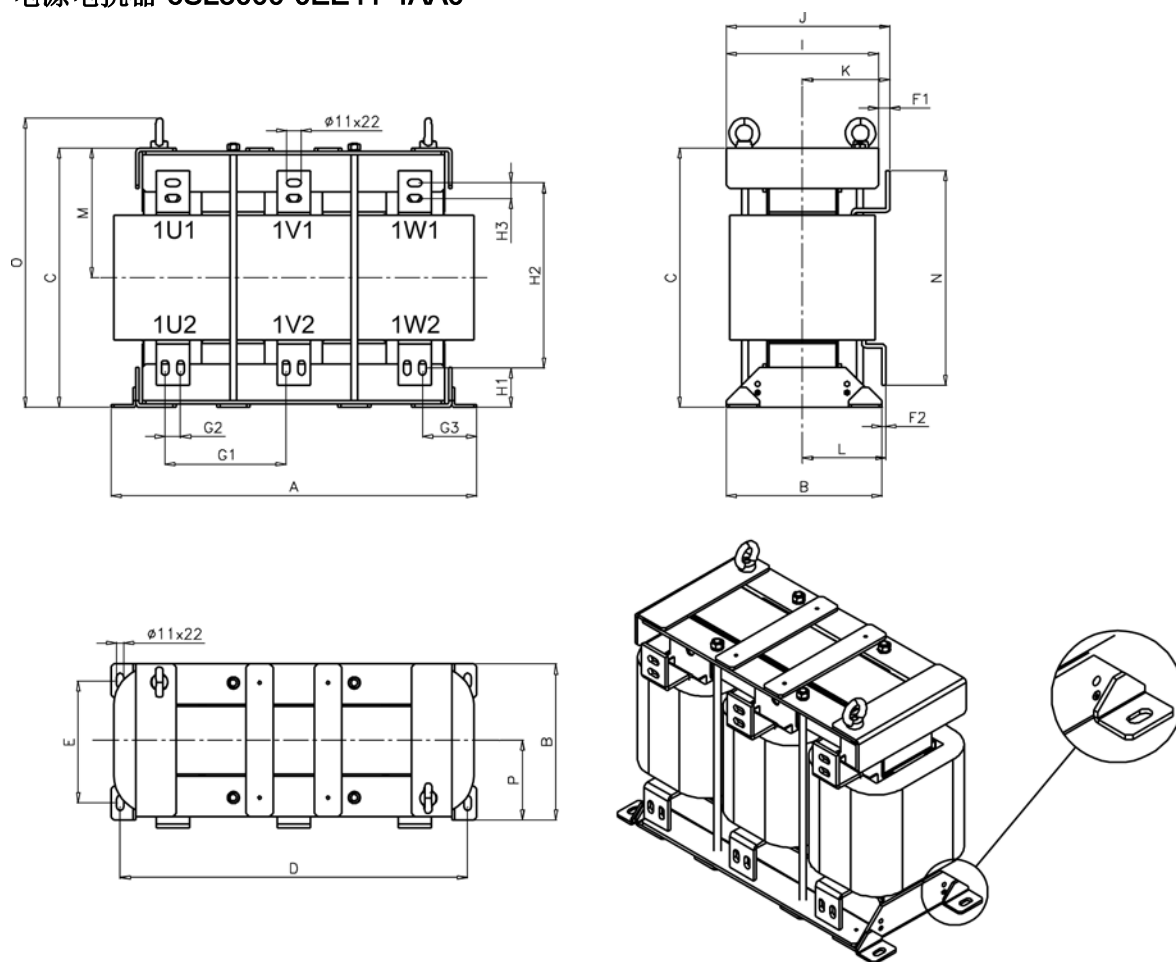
电源电抗器 6SL3000-0EE41-4AA0 的外形尺寸图
